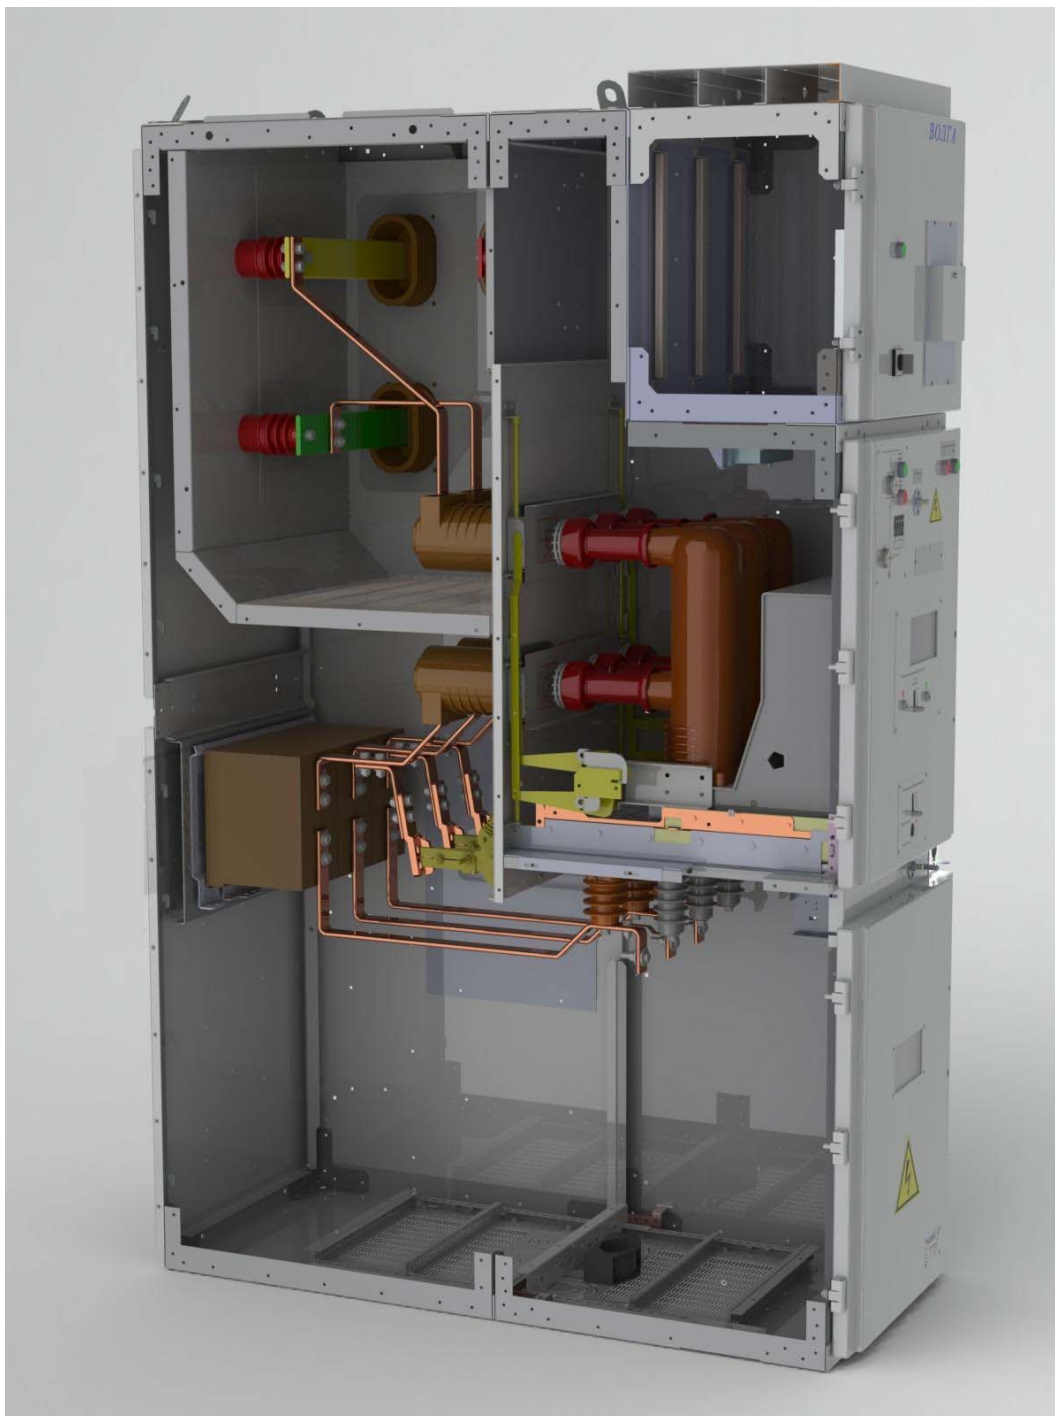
Общий вид внутреннего устройства ячейки КРУ
